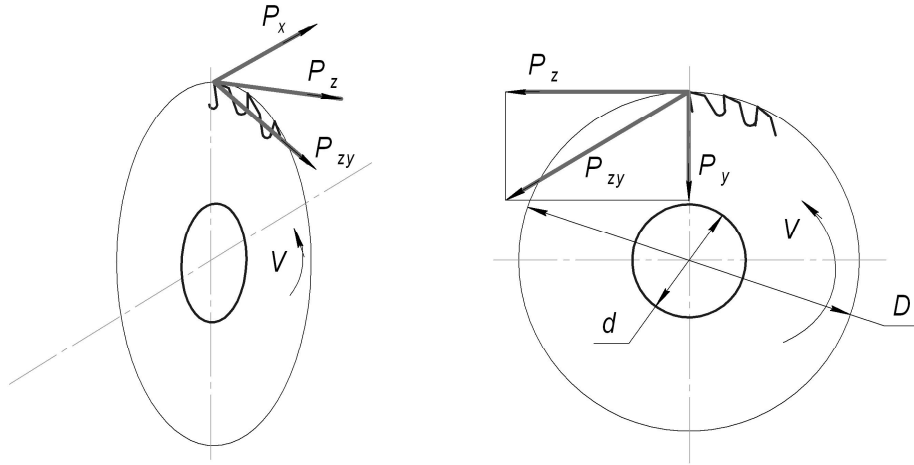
Схема сил, які діють на оправку під час фрезерування
